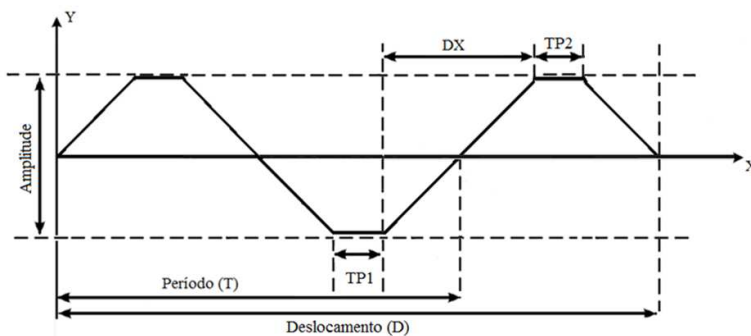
Tecimento trapezoidal da tocha de soldagem
